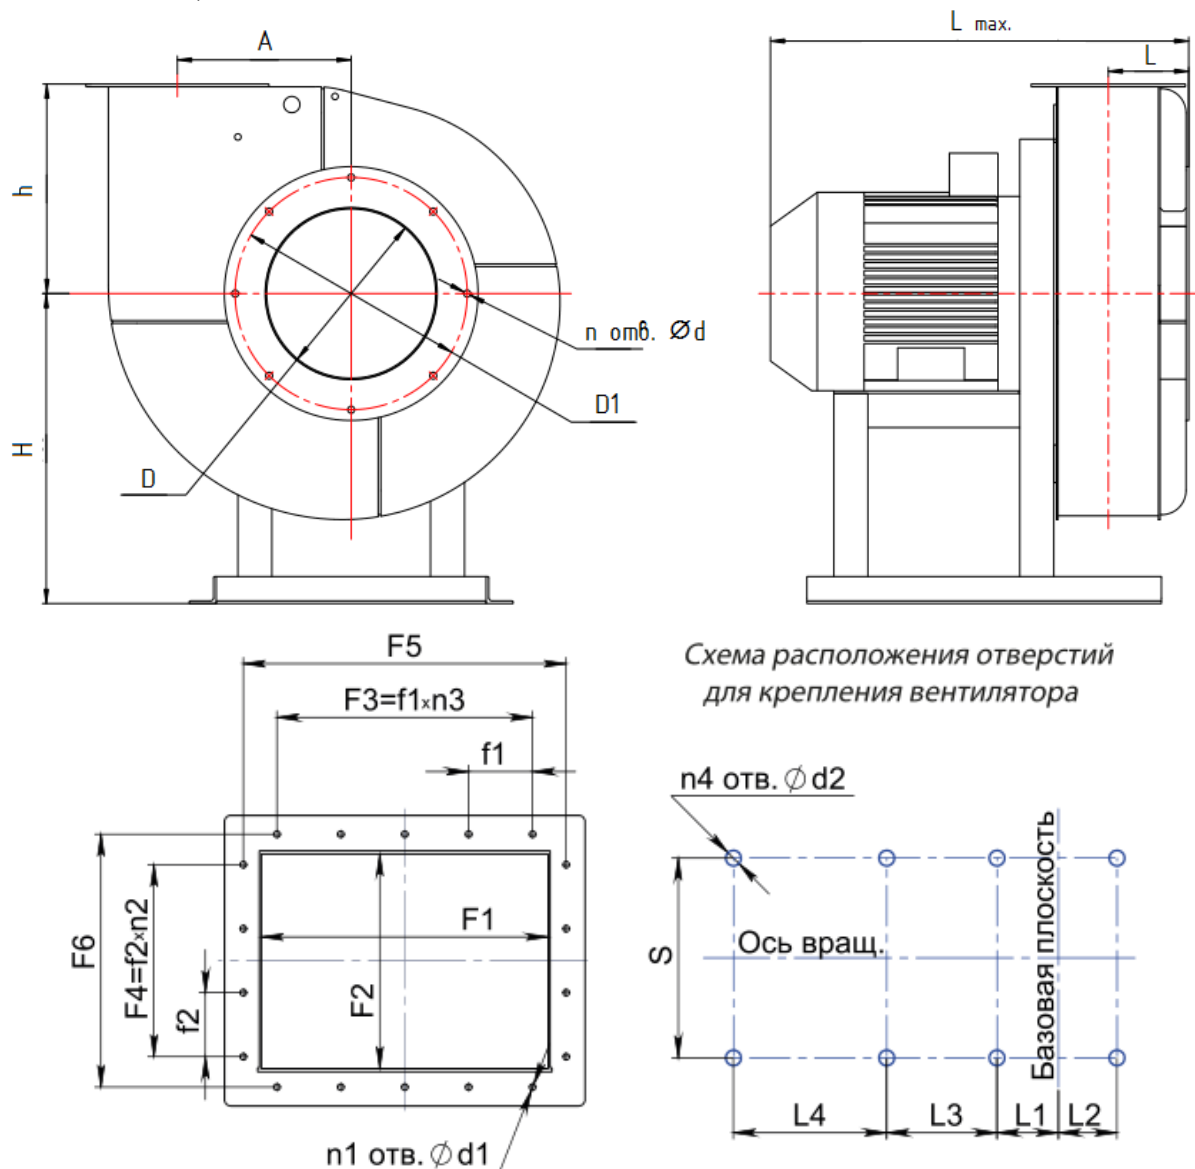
габаритно-присоединительные размеры вентилятора
